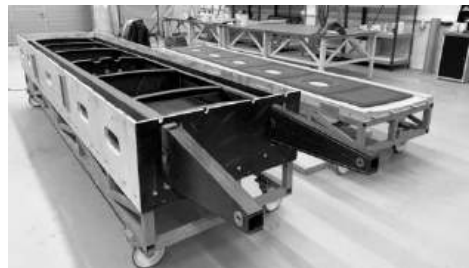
Приспособления для совмещения верхней и нижней матриц обшивки
